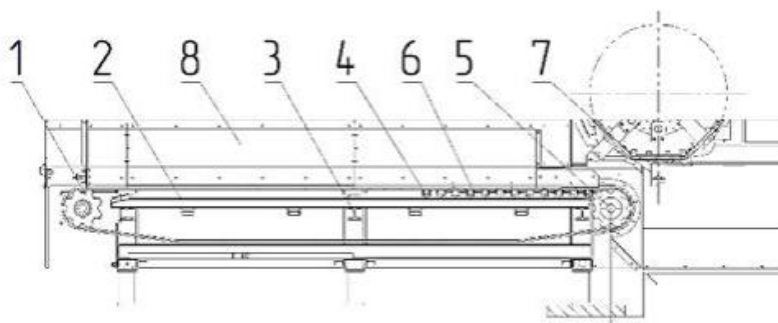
Устройство конвейера-разрывателя пакетов компании «Matthiessen»:
